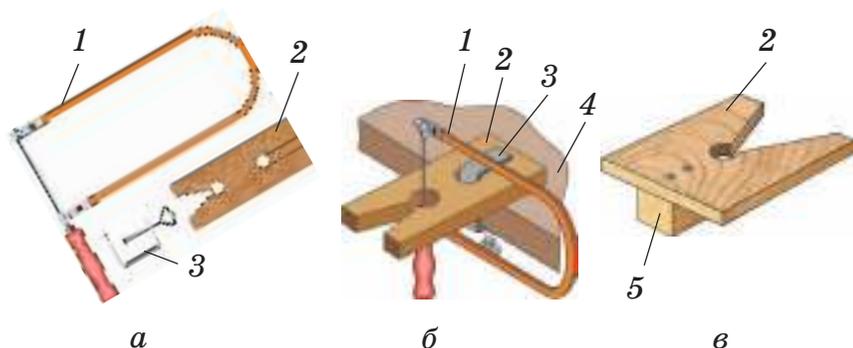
Ручной лобзик и приспособления для выпиливания:
